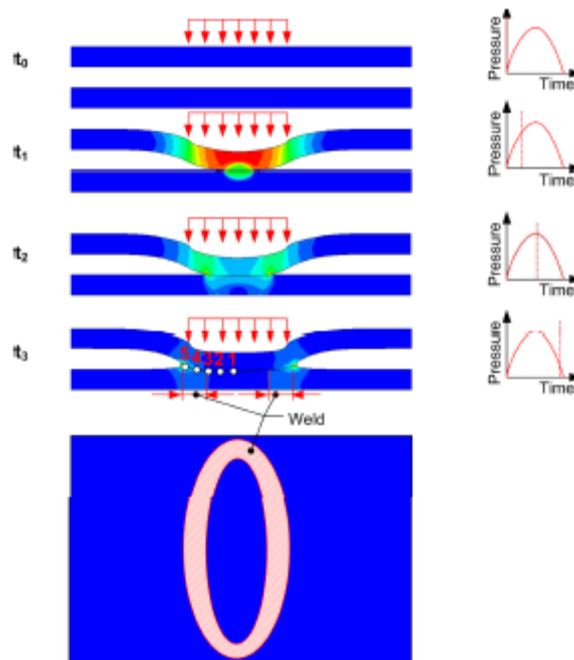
Ablauf des Magnetimpulsschweißens [74]
